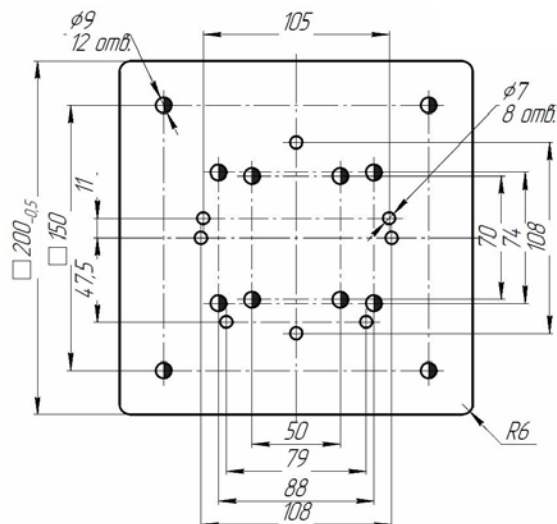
Внешний вид и габаритные размеры установочной площадки
